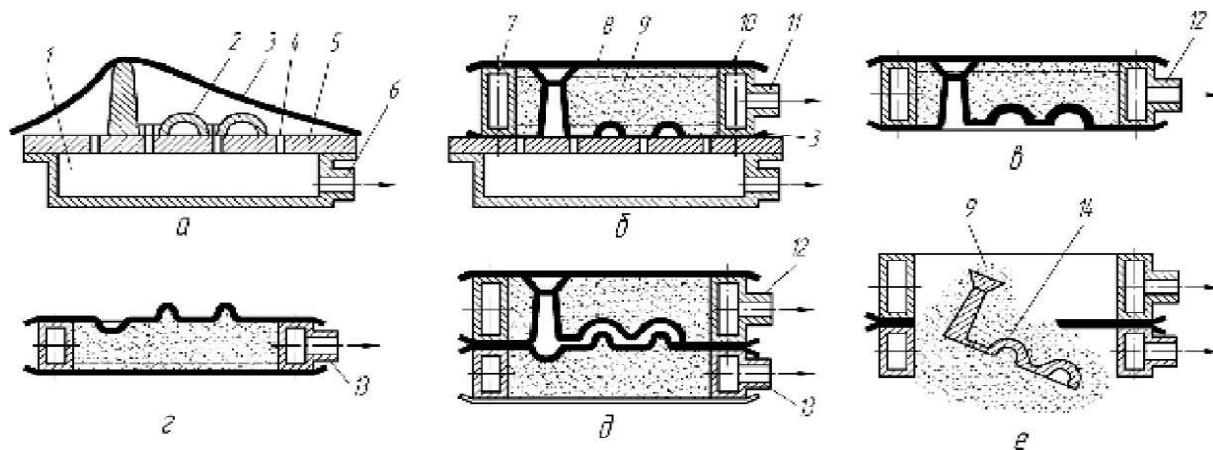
Последовательность операций при вакуумно-пленочной формовке:
